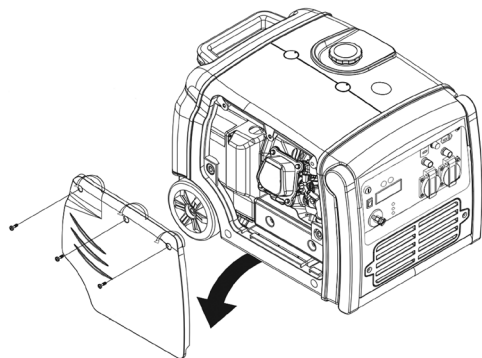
Removendo a tampa de manutenção do filtro de ar
